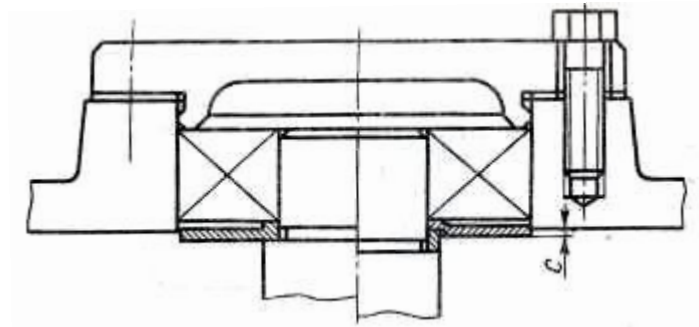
Схема крепления подшипниковой крышки стяжными болтами.
